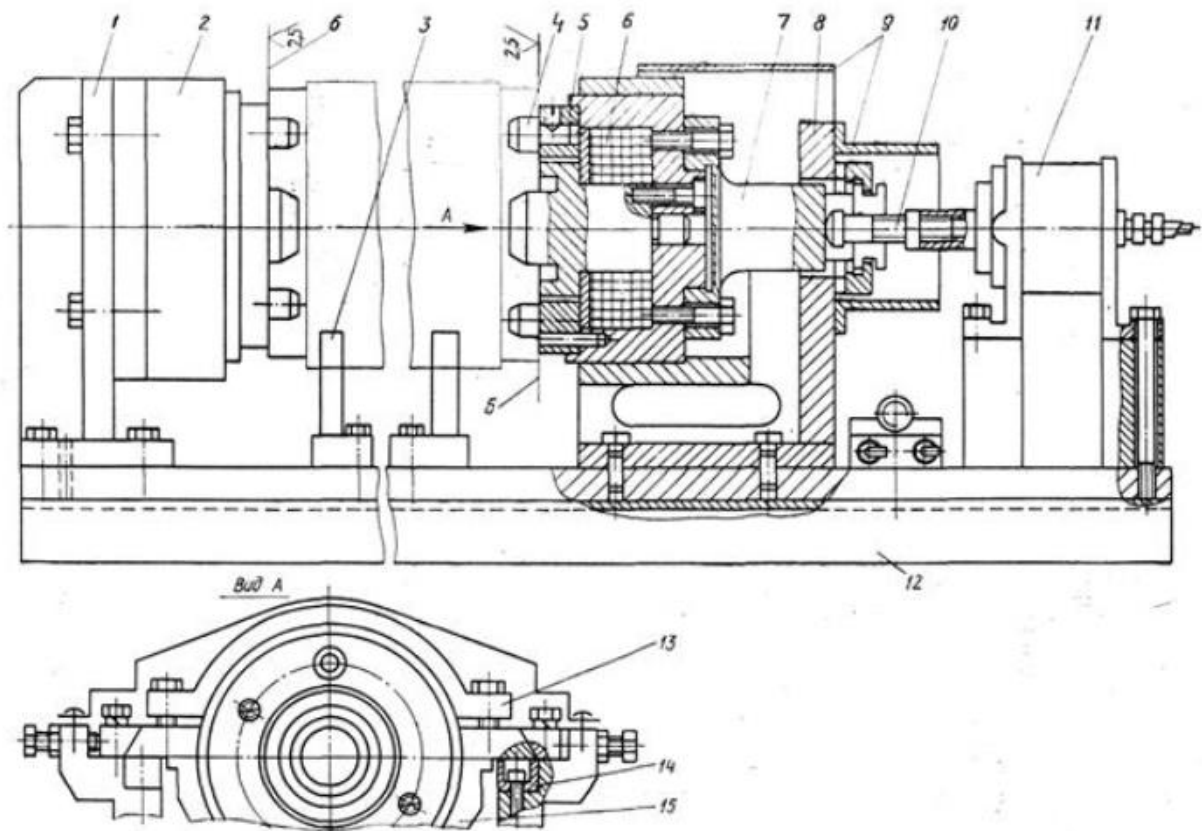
Пристрій для збирання та зварювання глушника
